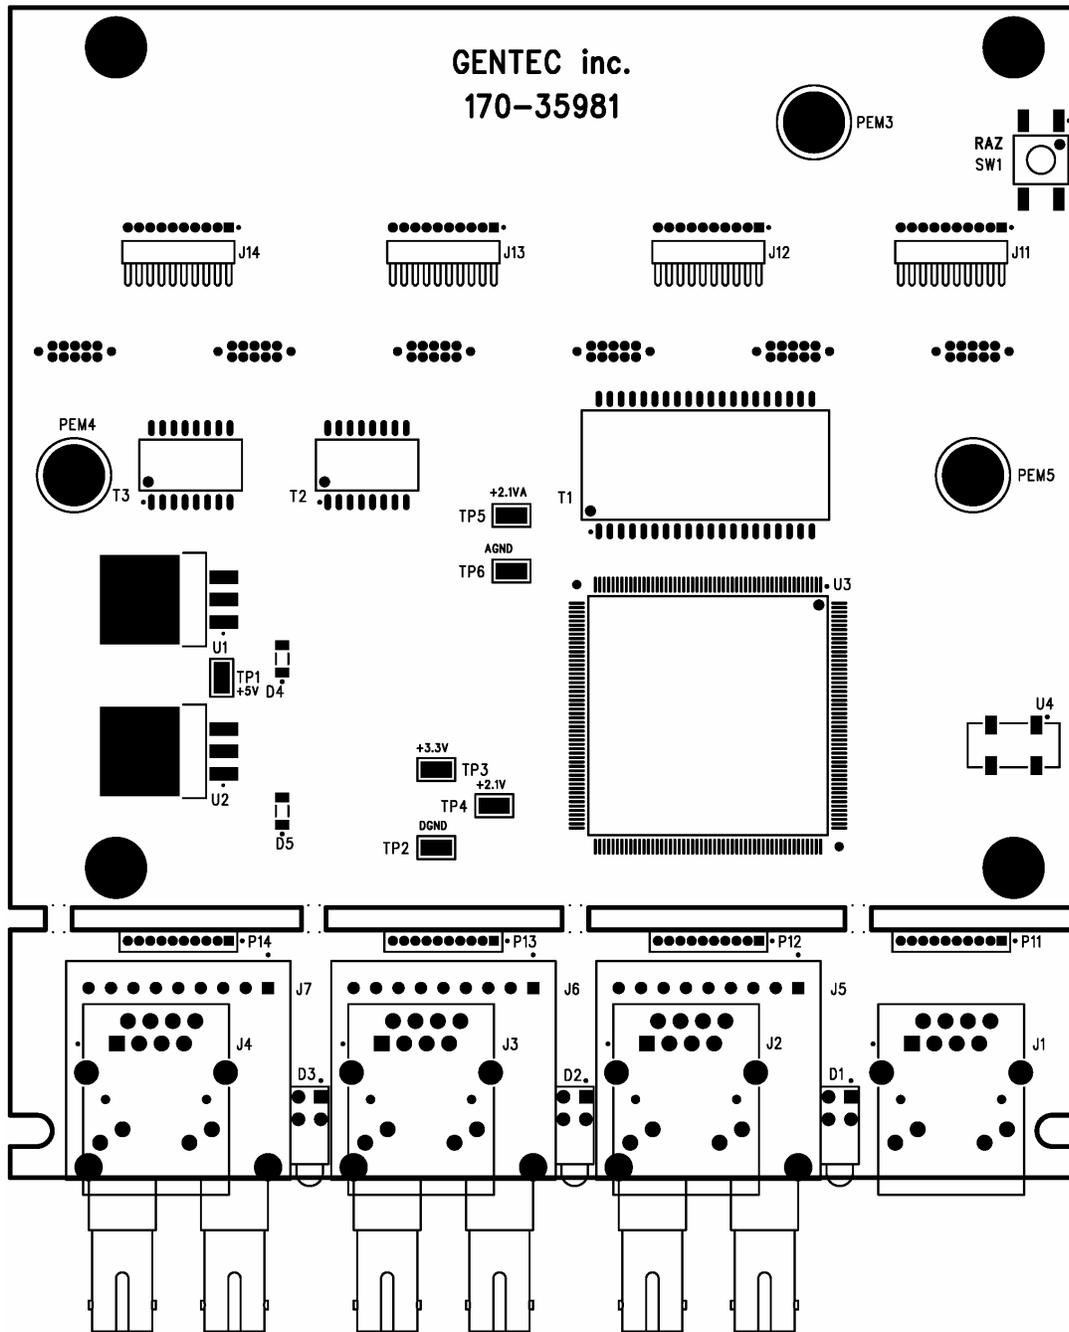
Schéma d'encombrement de la CCE3 (vue de dessus)
